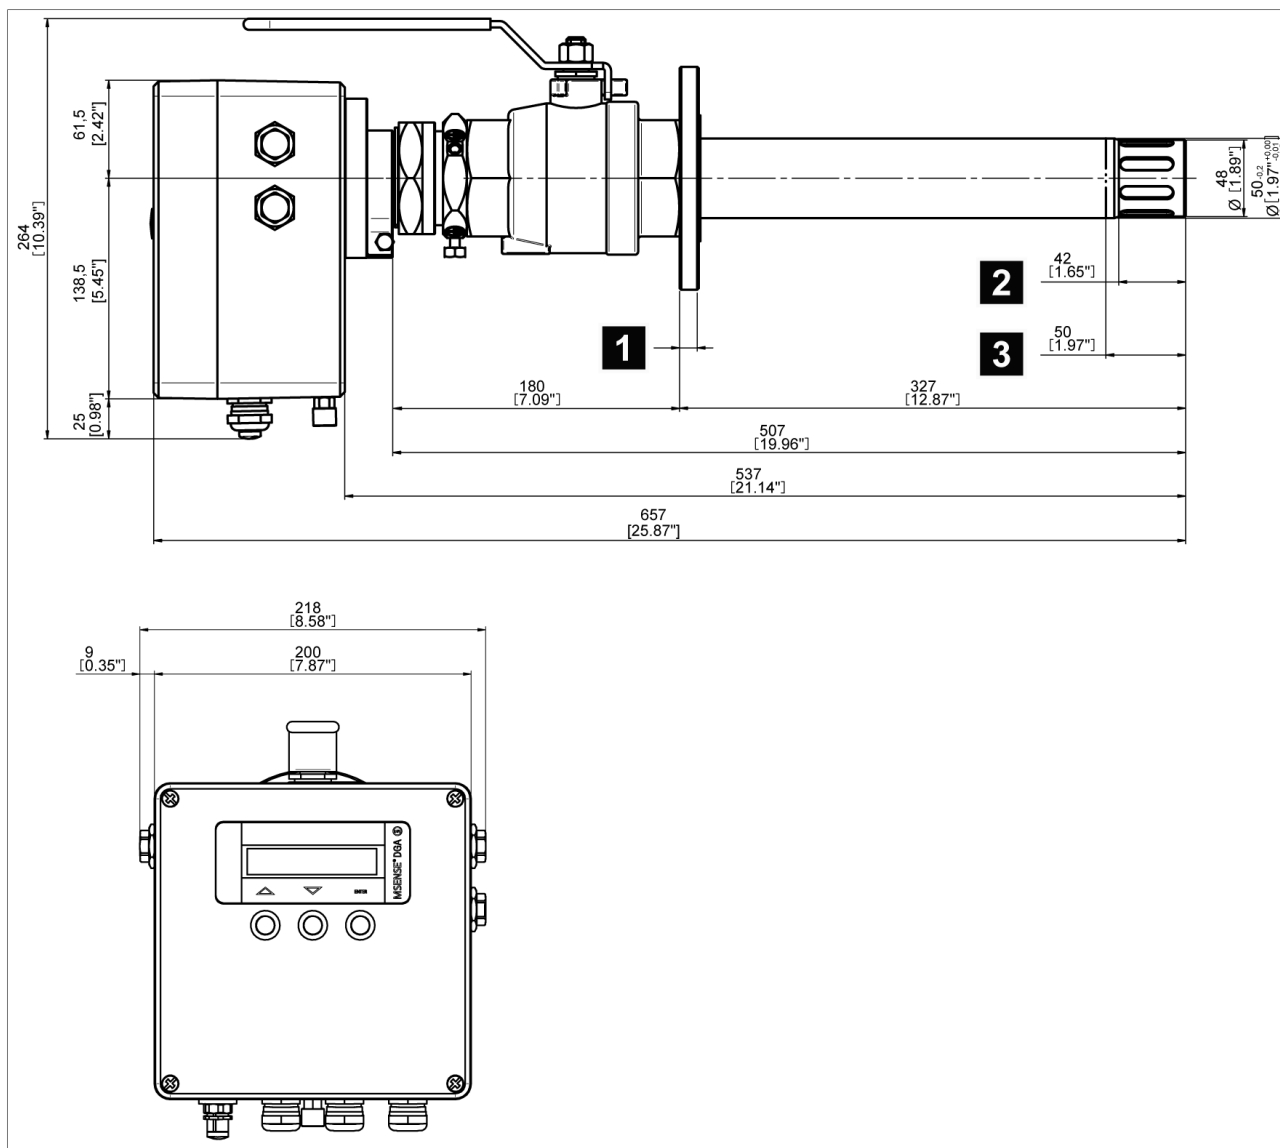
Dimensioni apparecchio con tubo di misura di 507 mm
